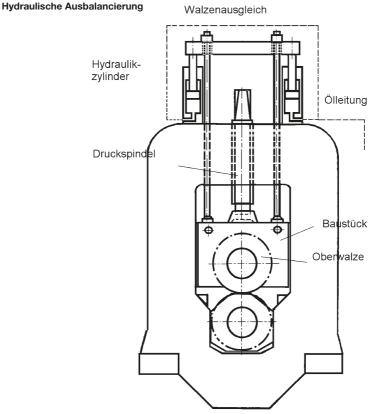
Walzenausgleich mit hydraulischem Gewichtsausgleich
